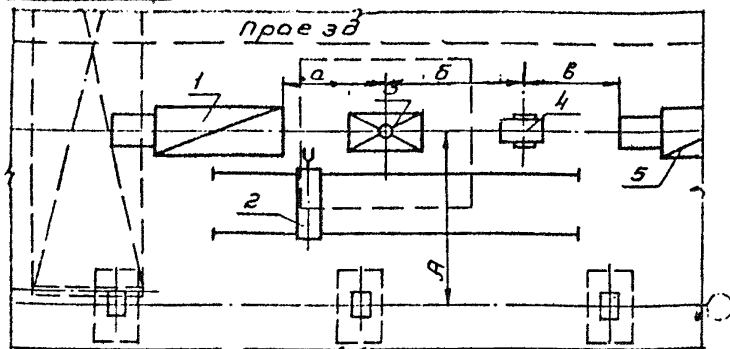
Схема расположения штамповочных линий на базе ШМ с напольным манипулятором:
